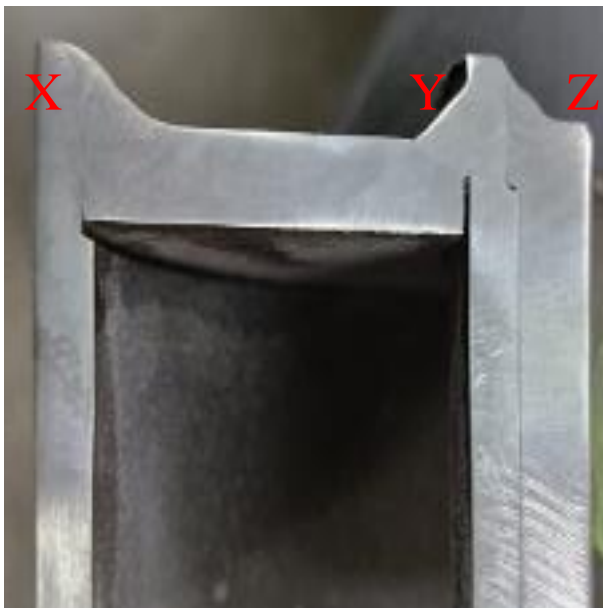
corpo de prova 2 solda X,Y e Z.
